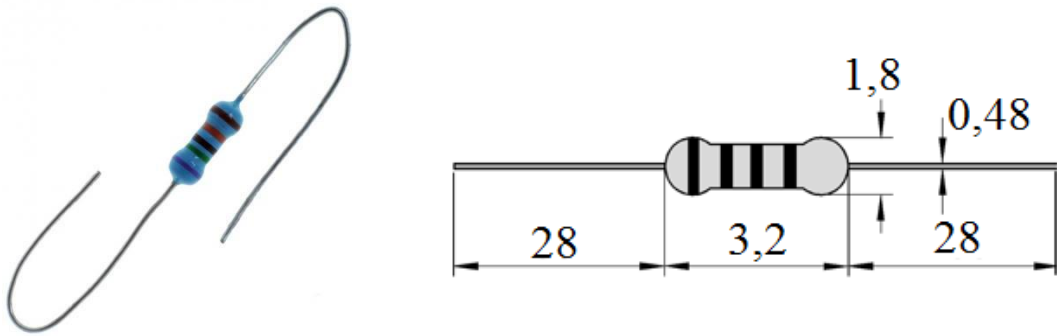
Габаритні розміри постійного резистора типу MF-25
